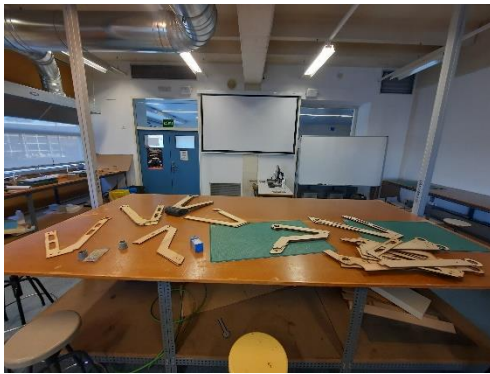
Montaje maqueta en los laboratorios de la ETSID.
